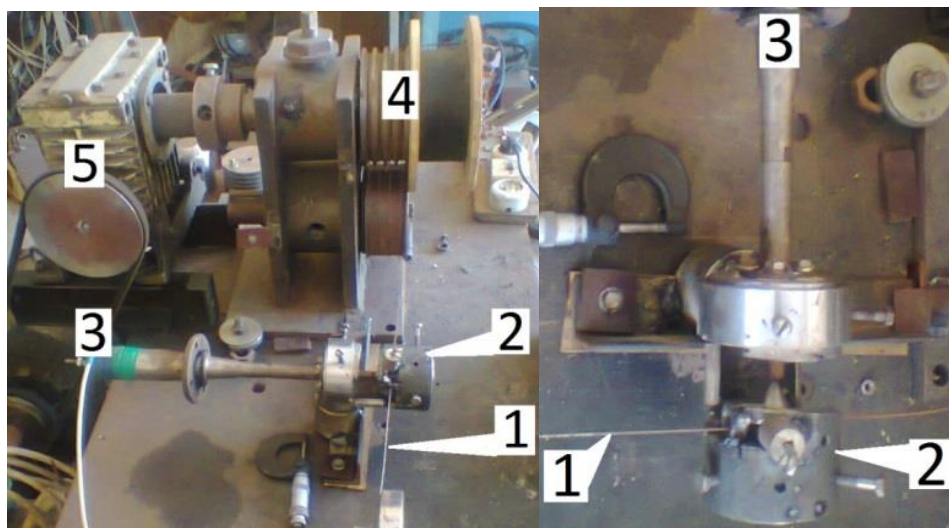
Лабораторная установка для исследования параметров бесфильтрного волочения проволоки: 1 – проволока, 2 – инструмент для бесфильтрного волочения, 3 – генератор ультразвука, 4 – барабаны натяжной станции, 5 – привод установки
